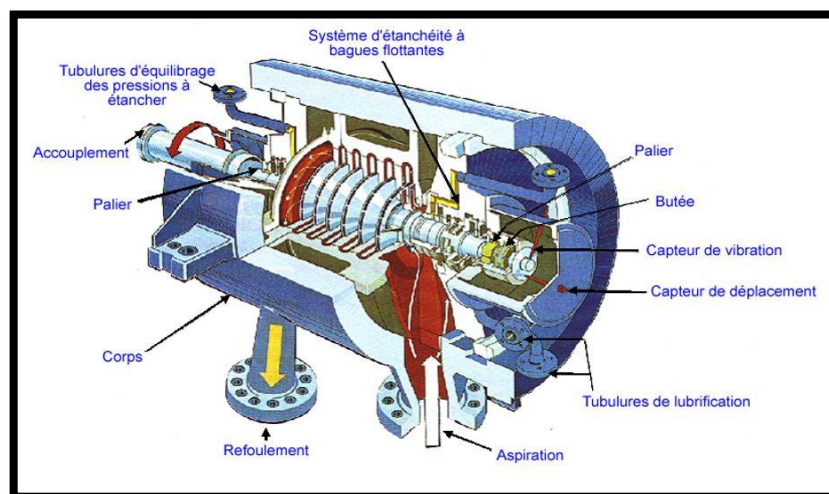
Compresseur centrifuge avec plan de joint vertical (Barrel) [11]
